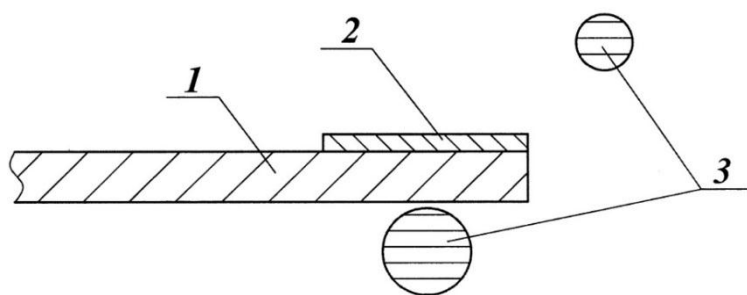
Схема індукційного наплавлення: 1 – деталь; 2 – порошкоподібний твердий сплав; 3 – двовитковий кільцевий індуктор
